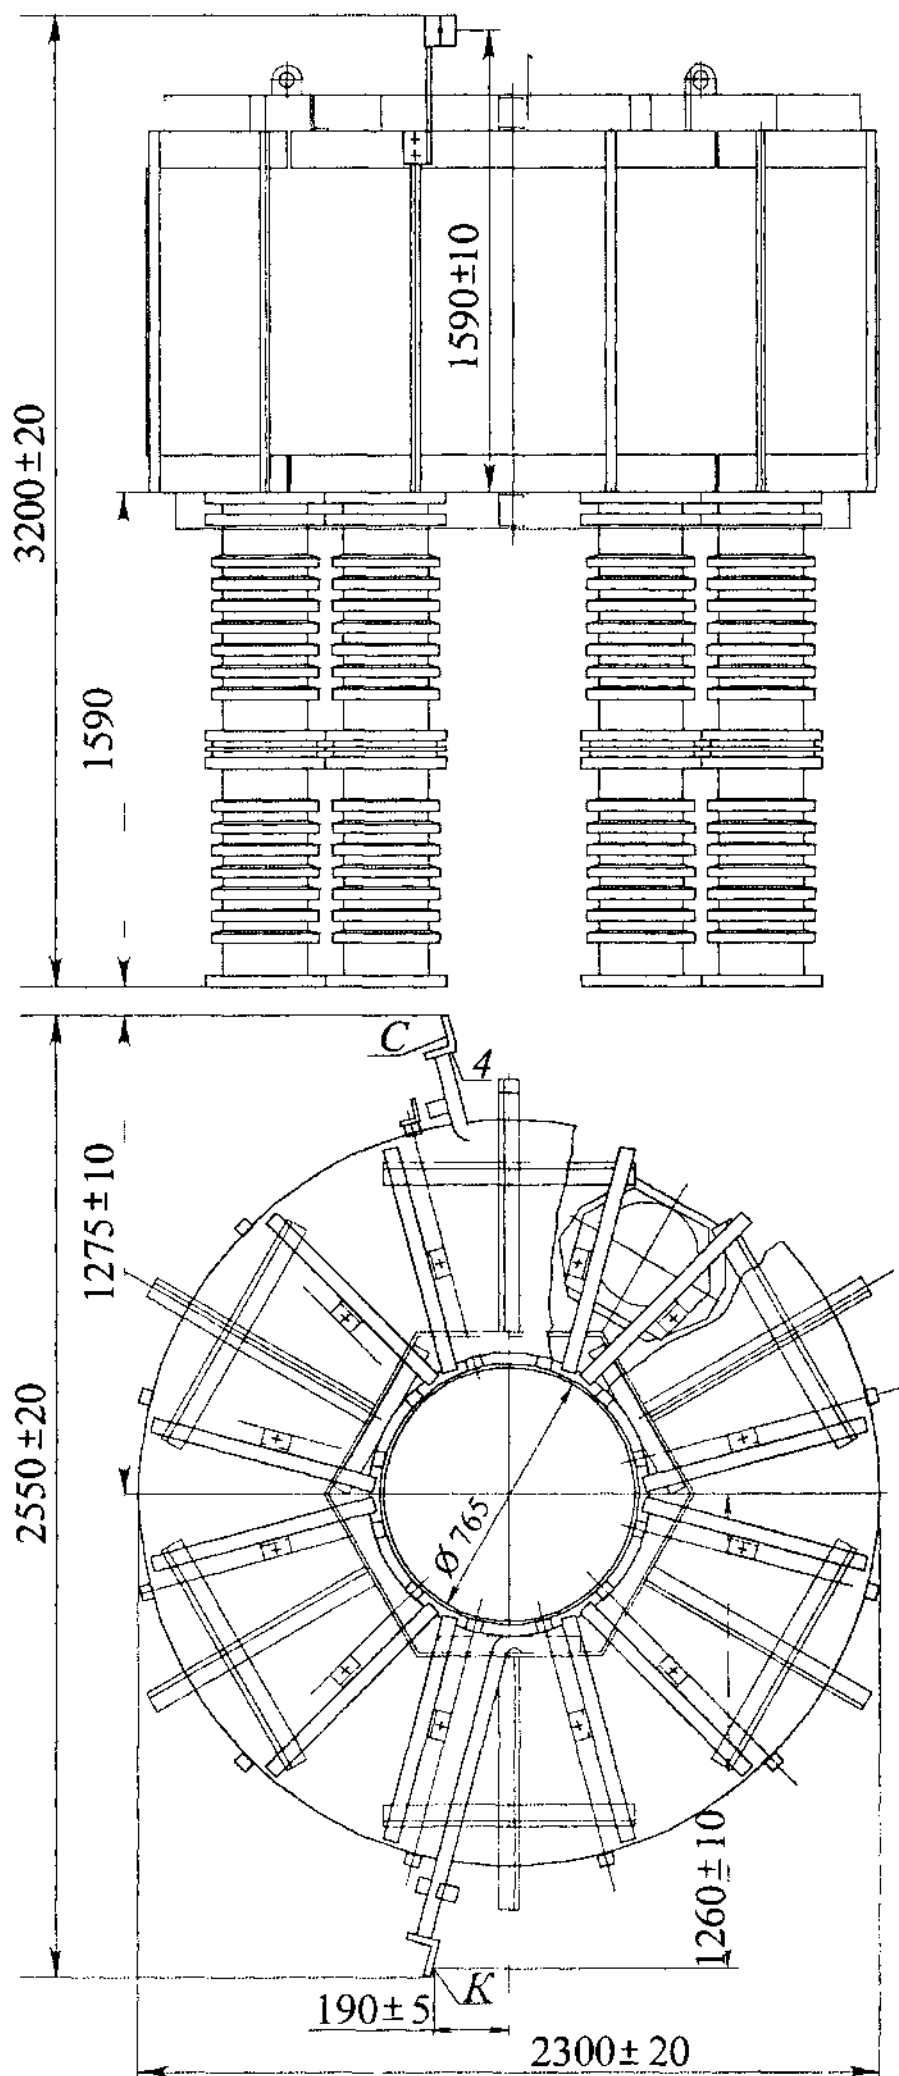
12 Конструкция фазы сухого реактора типа РКРС-7000/35
